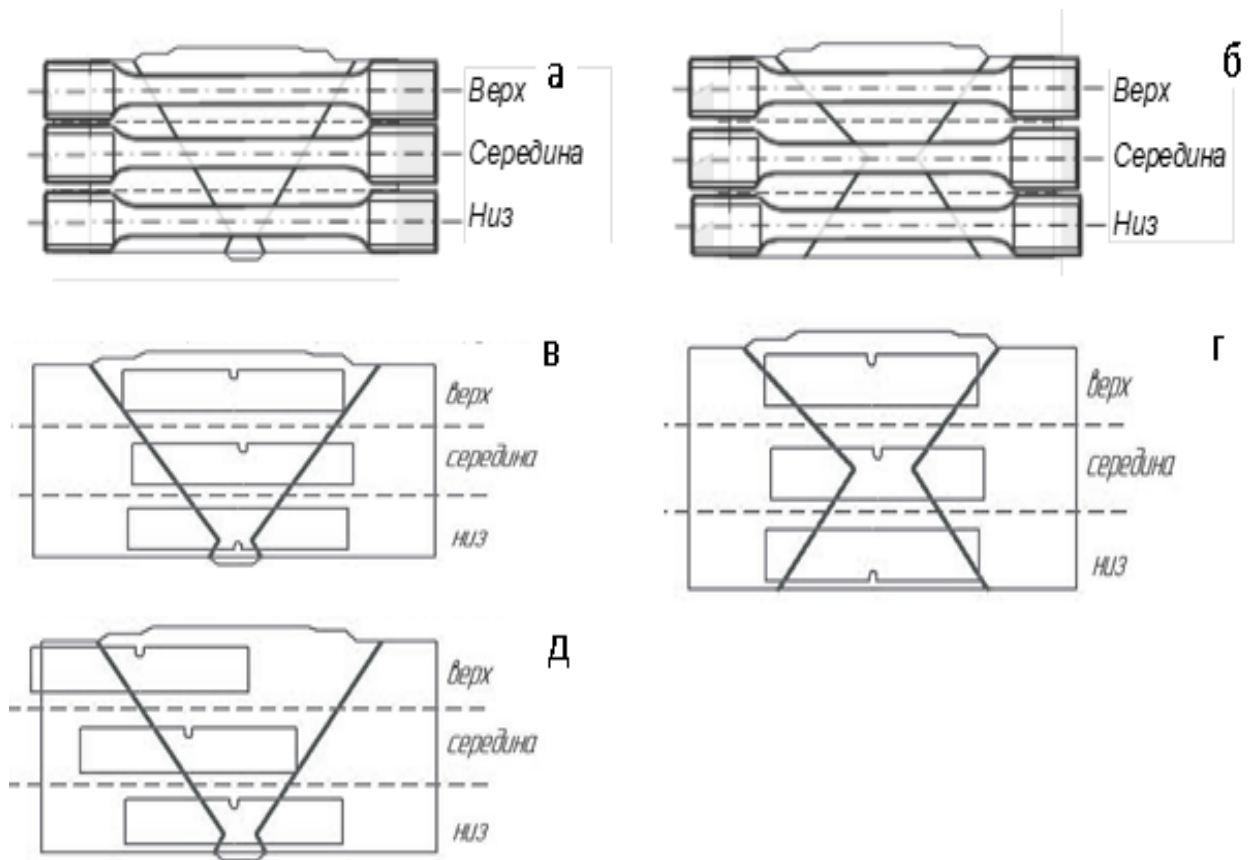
Схемы вырезки образцов из сварных пластин: а, в, д – СС-V; б, г – СС-X.
